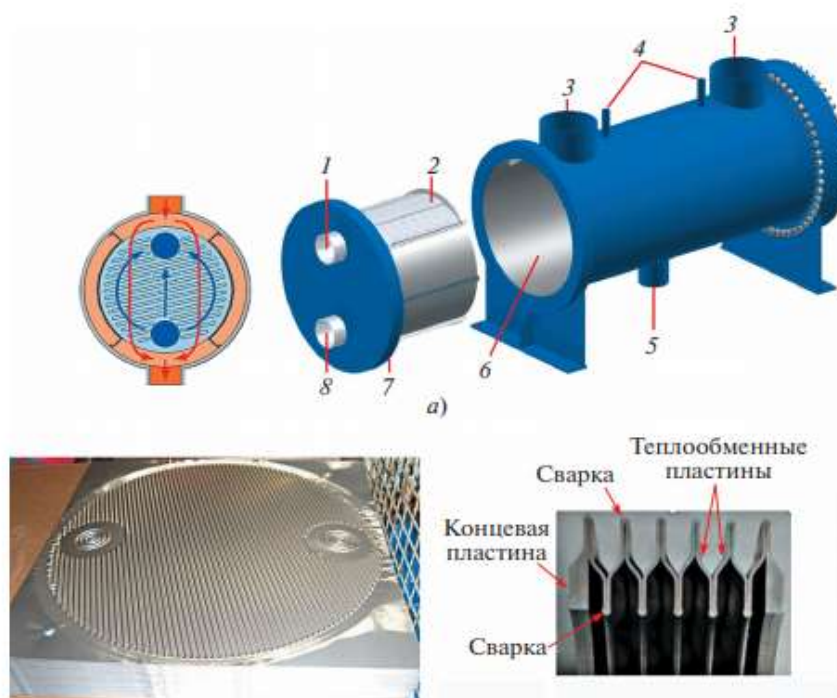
Пластинчатый подогреватель низкого давления производства Tranter Inc. [3].
